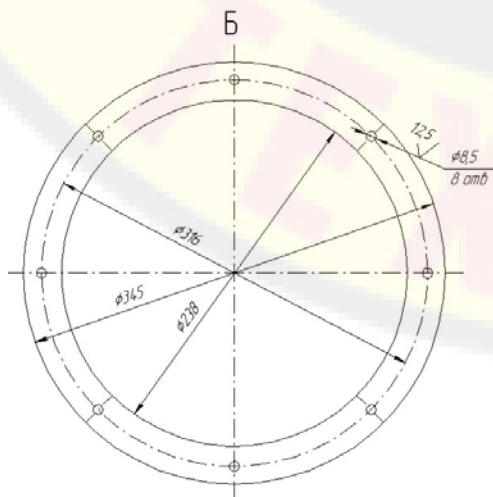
Установка для мойки агрегатов автомобилей.
